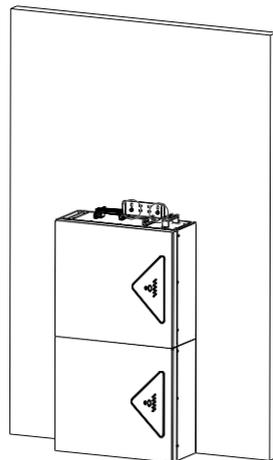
Installation de la batterie – Installation de la deuxième batterie
